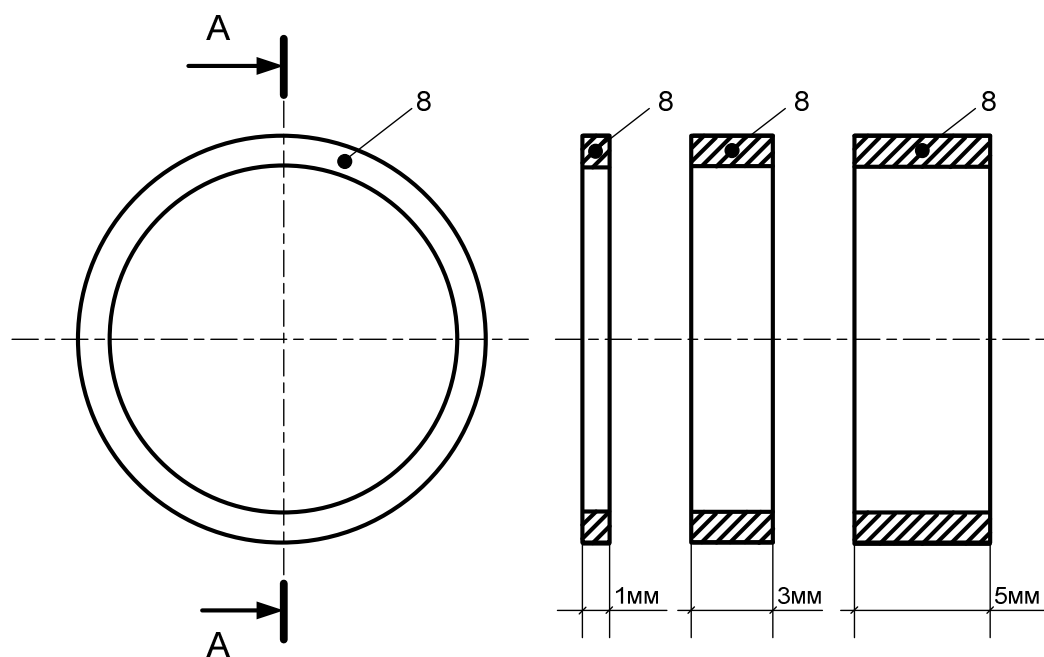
Общий вид регулировочных колец с их разрезом по сечению Б-Б
